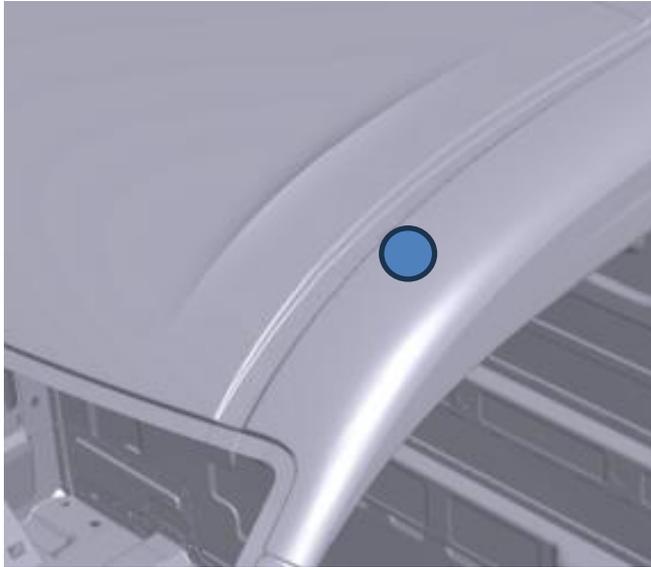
predisposizione passacavi per luci di ingombro – apertura nella zona del tetto (lato sinistro nella figura)
